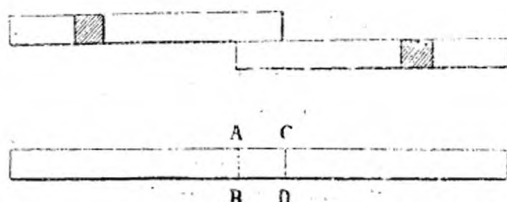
SOUDURE PAR CONTACT OU PAR APPROCHE.
